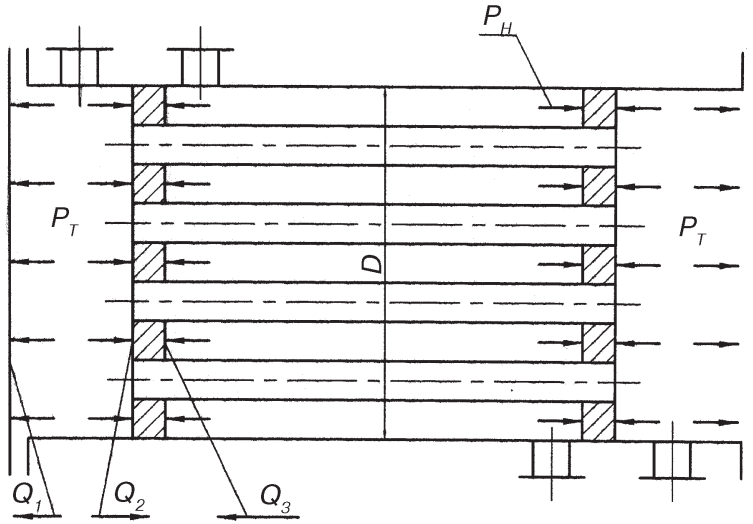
Схема к расчету усилий от внутреннего давления
